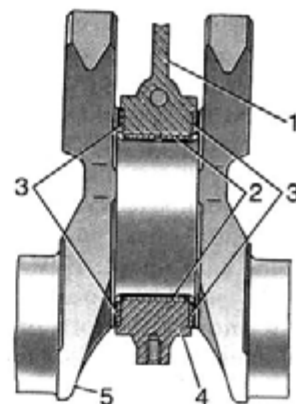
Средний (упорный) коренной подшипник коленчатого вала:
